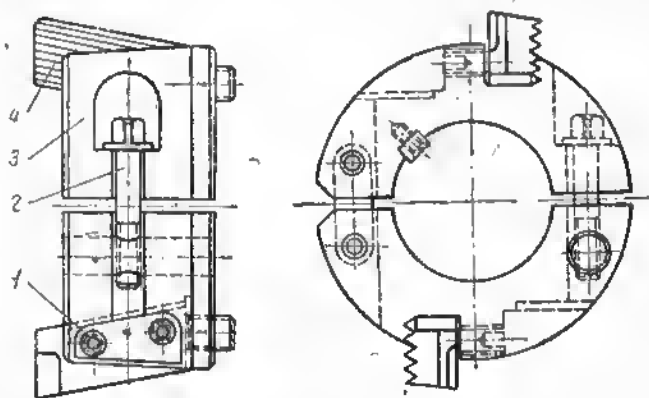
Обработка деталей двухрезцовыми блоками:
